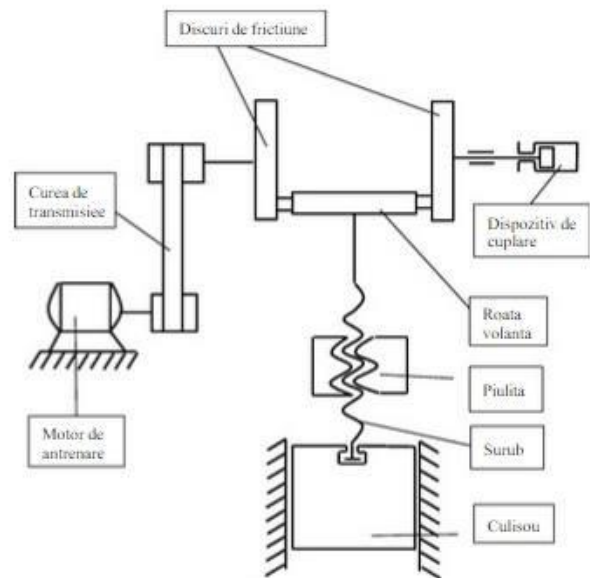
Presa mecanică cu șurub cu fricțiune cu discuri frontale
